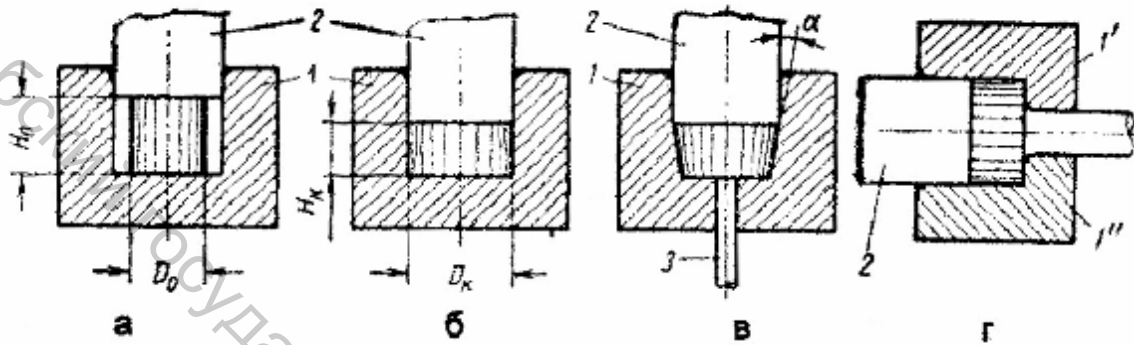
Схемы штамповки в закрытых штампах: 1 — матрица, 2 — пуансон, 3 — выталкиватель
